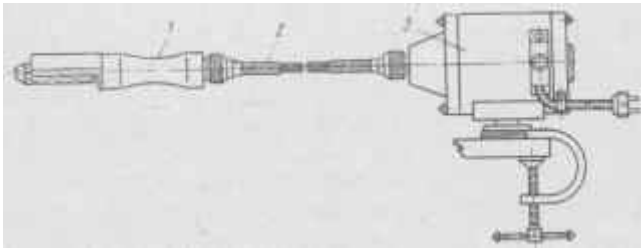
Рыбоочиститель РО-1: 1 - скребок с рукояткой; 2 - гибкий вал; 3 - электродвигатель.
